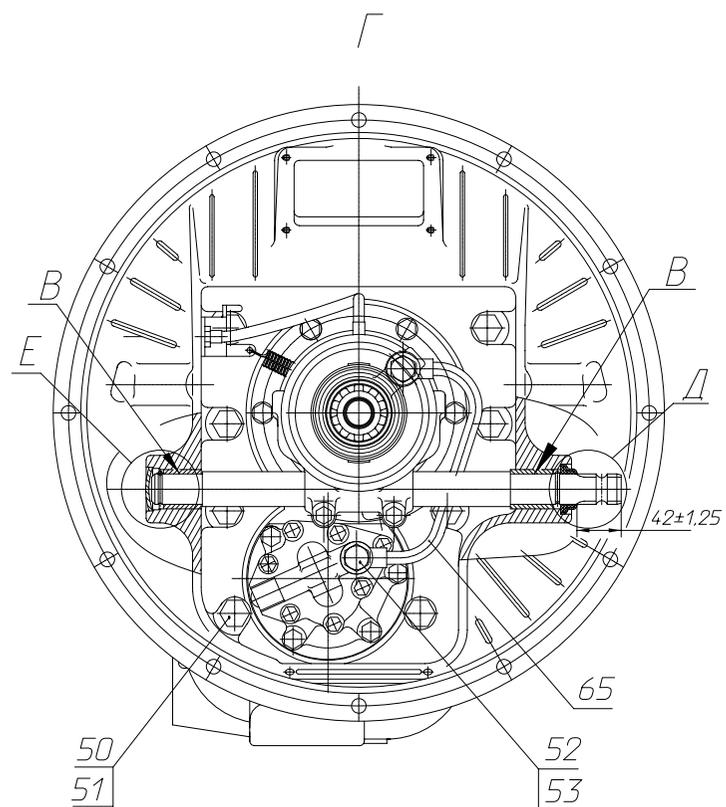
(продолжение 1) – Коробка передач ЯМЗ-239 (вид спереди и на бобышки картера сцепления под вал сцепления)
